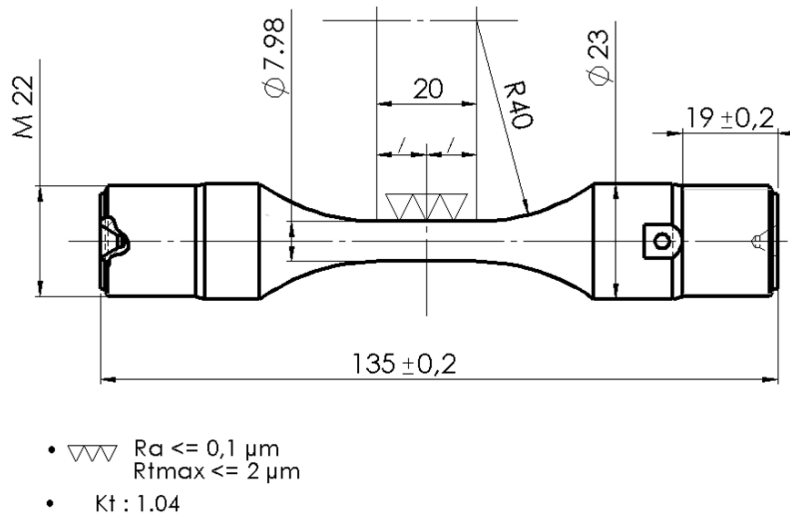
Géométrie des éprouvettes des essais de fatigue-corrosion
